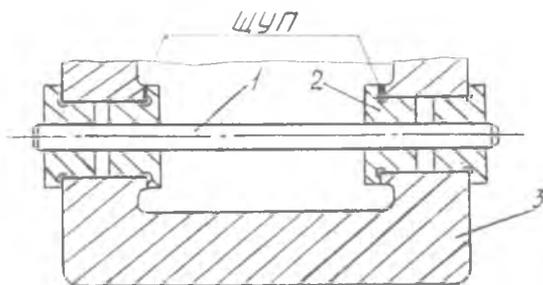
Схема проверки неперпендикулярности торцов к осям отверстий: *1* — валок; *2* — втулка; *3* — проверяемая деталь
